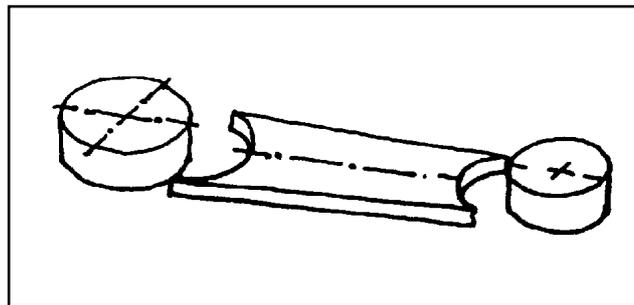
8: Einzelteile für geschweißten Hebel
